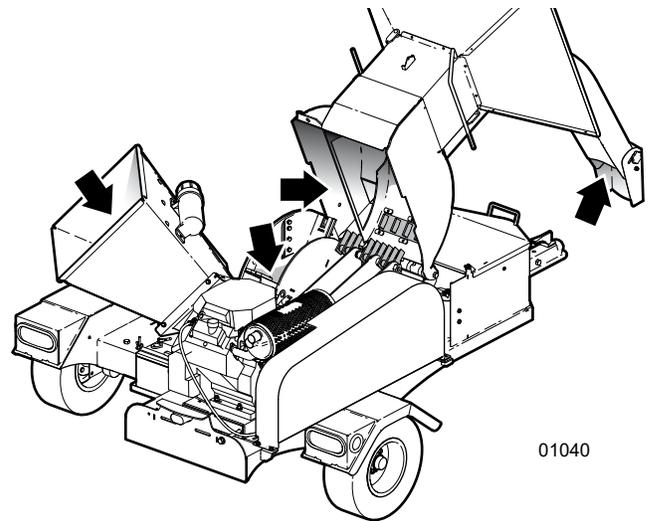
Boulon supérieur du boîtier du rotor (typique)
